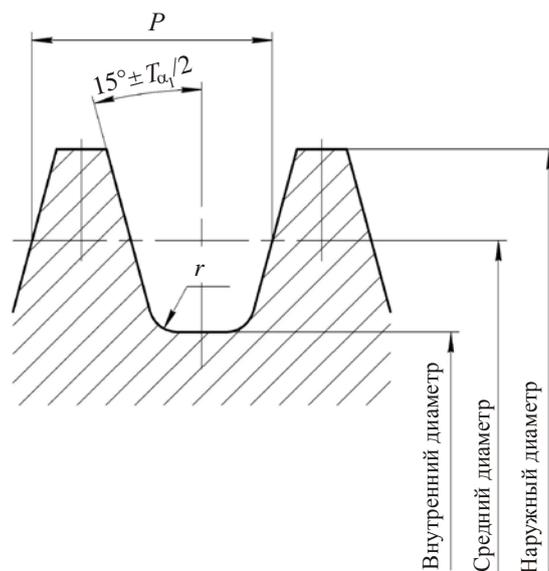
Полный профиль резьбы калибров-пробок для контроля внутренней трапецевидальной резьбы
